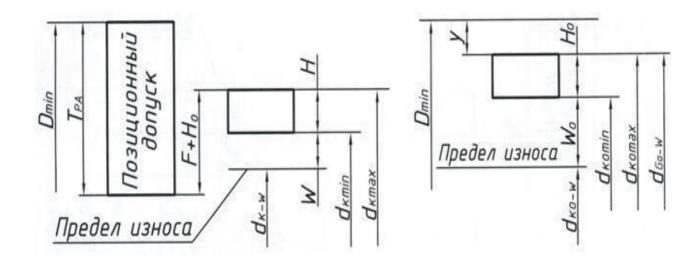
Схема расположения полей допусков калибров для контроля отверстий при наличии базового отверстия
